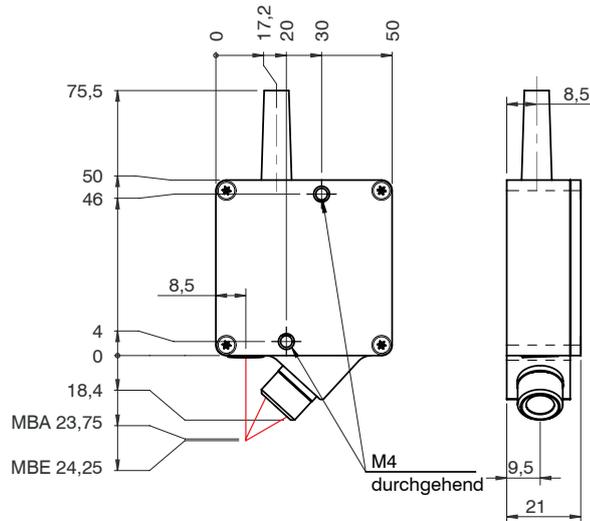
Maßzeichnung LD1610-0,5 und LD1630-0,5
